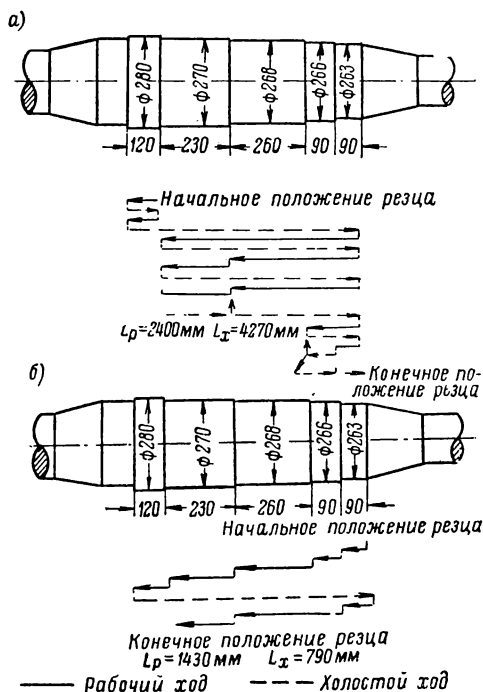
Схематические изображения перемещений резца при обработке центральной части вала крупной электрической машины.
